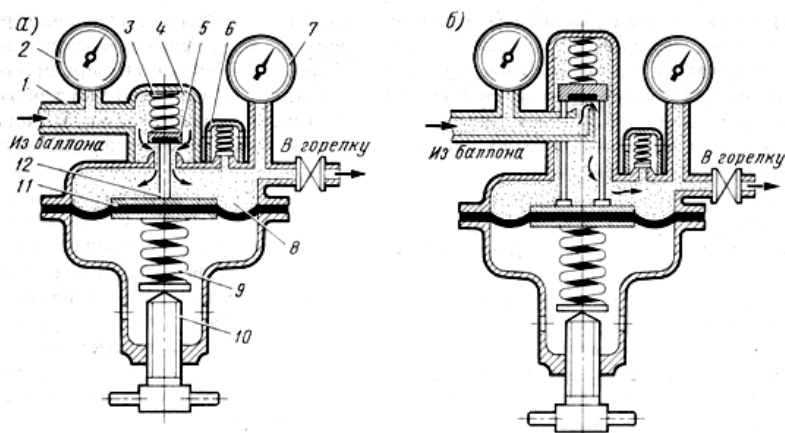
Схема редуктора обратного (а) и прямого (б) действия:
